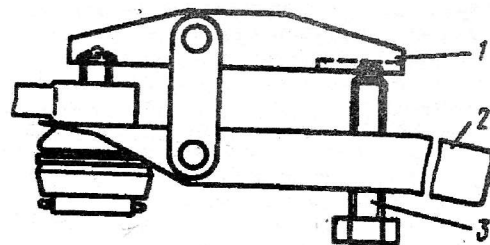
Выпрессовка пальца шарового шарнира из поворотных рычагов и бобышек тяги сошки съемником 7823-6899:
